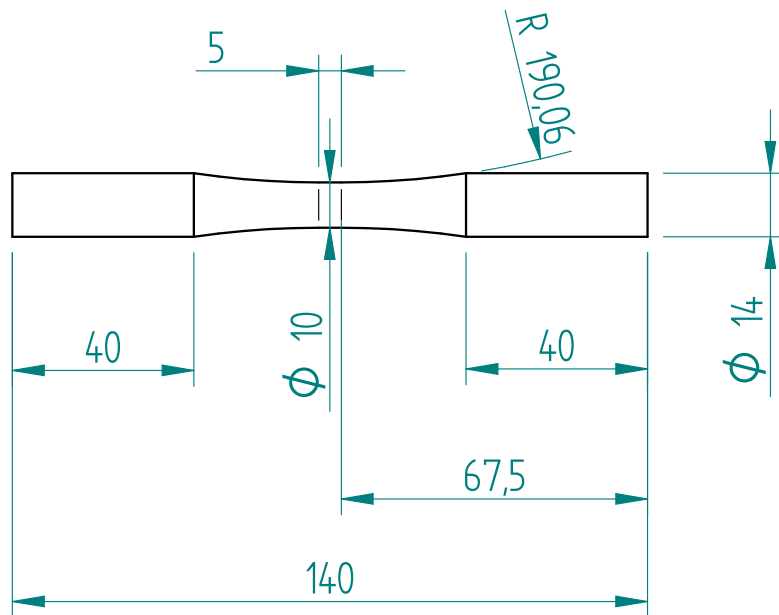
Plan des éprouvettes de fatigue (dimensions en mm)
